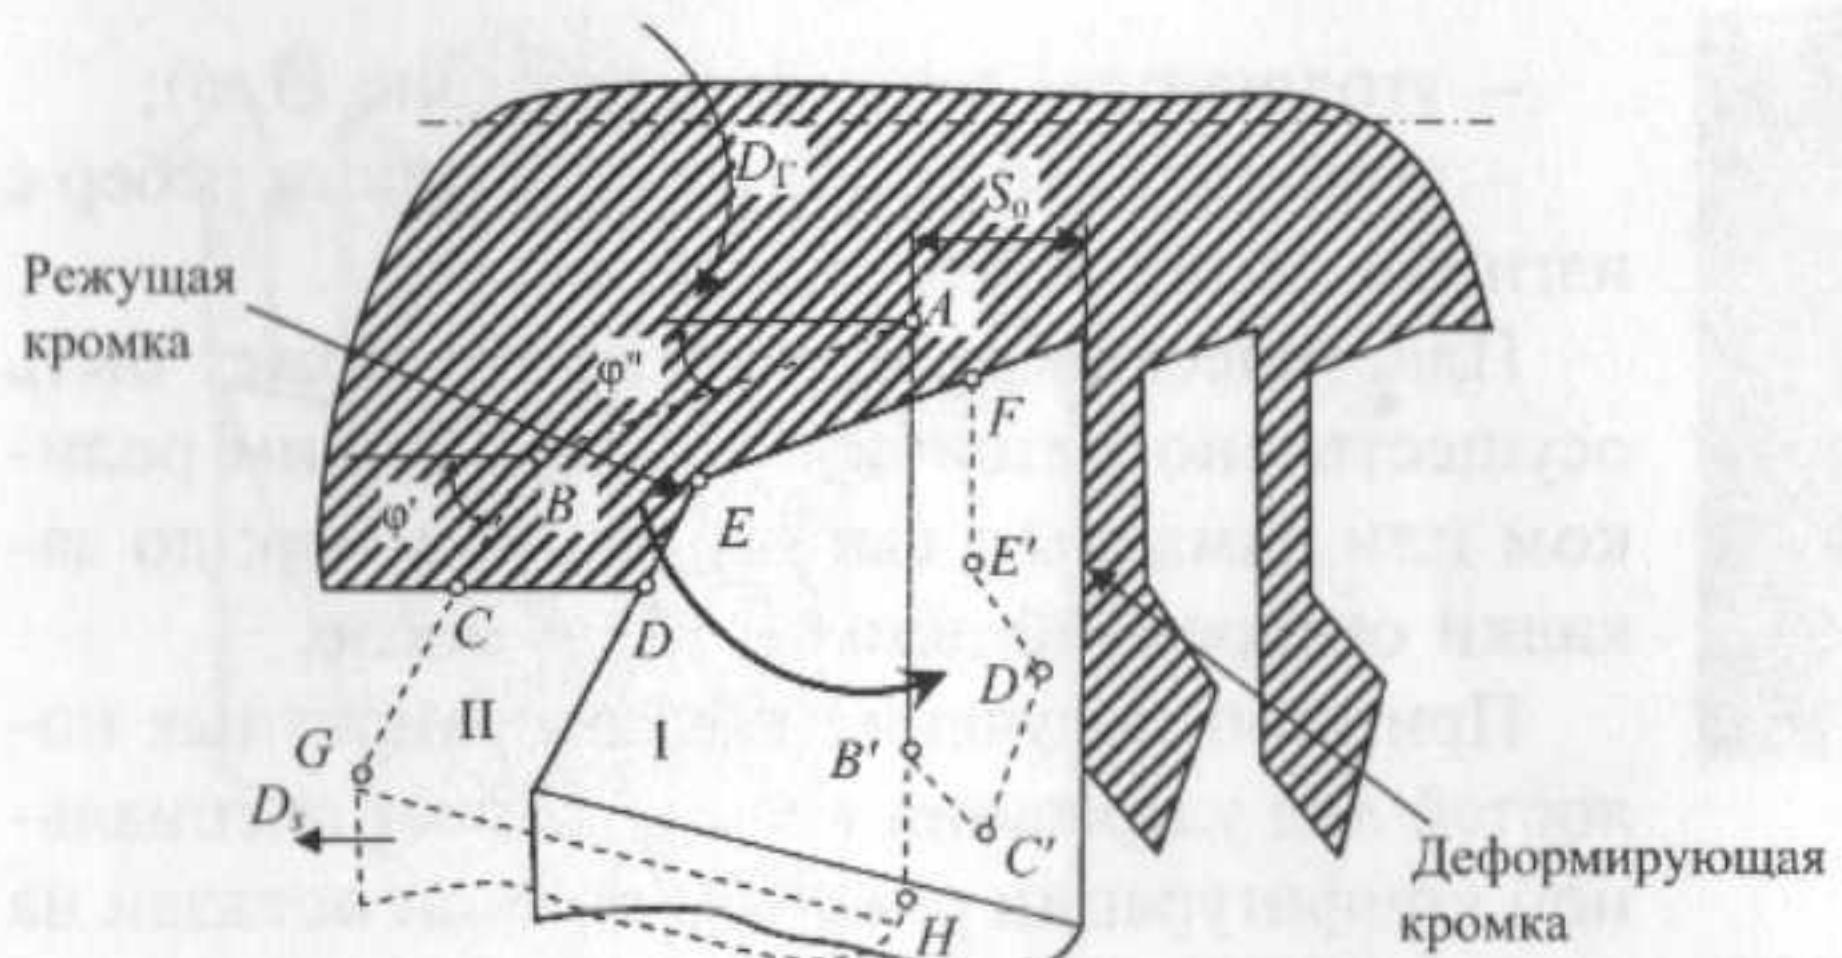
Принцип формирования подповерхностных полостей инструментом для ДР с двойной режущей кромкой
